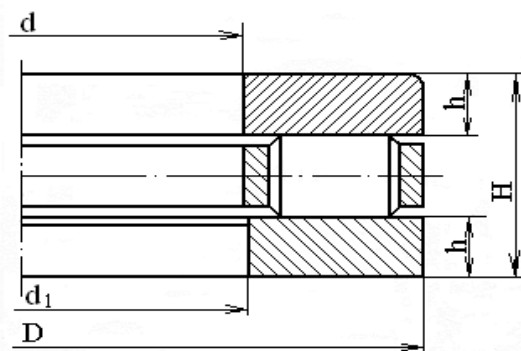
Подшипник роликовый упорный, однорядный
